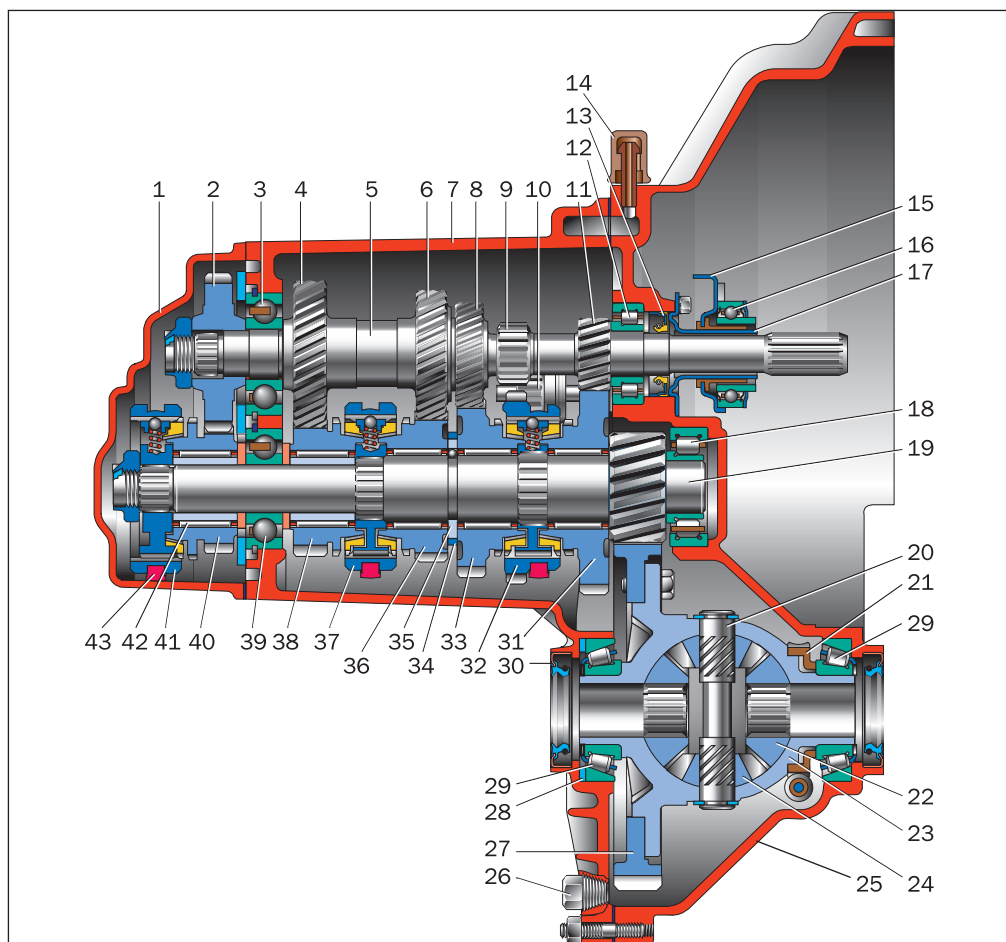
Пятиступенчатая двухвальная коробка передач легкового автомобиля с поперечным расположением двигателя: 1 — задняя крышка картера коробки передач; 2 — ведущая шестерня V передачи; 3 — шариковый подшипник первичного вала; 4 — ведущая шестерня IV передачи первичного вала; 5 — первичный вал; 6 — ведущая шестерня III передачи первичного вала; 7 — картер коробки передач; 8 — ведущая шестерня II передачи первичного вала; 9 — шестерня заднего хода; 10 — промежуточная шестерня заднего хода; 11 — ведущая шестерня I передачи первичного вала; 12 — роликовый подшипник первичного вала; 13 — сальник первичного вала; 14 — сапун; 15 — фланец муфты; 16 — подшипник выключения сцепления; 17 — направляющая втулка муфты; 18 — роликовый подшипник вторичного вала; 19 — вторичный вал; 20 — ось сателлитов; 21 — ведущая шестерня привода спидометра; 22 — шестерня полуоси; 23 — коробка дифференциала; 24 — сателлит; 25 — картер сцепления; 26 — пробка для слива масла; 27 — ведомая шестерня главной передачи; 28 — регулировочное кольцо; 29 — роликовый конический подшипник дифференциала; 30 — сальник полуоси; 31 — ведомая шестерня I передачи вторичного вала; 32 — синхронизатор I и II передач; 33 — ведомая шестерня II передачи вторичного вала; 34 — стопорное кольцо; 35 — упорное полукольцо; 36 — ведомая шестерня III передачи вторичного вала; 37 — синхронизатор III и IV передач; 38 — ведомая шестерня IV передачи вторичного вала; 39 — шариковый подшипник вторичного вала; 40 — ведомая шестерня V передачи вторичного вала; 41 — синхронизатор V передачи; 42 — игольчатый подшипник; 43 — вилка переключения передач
